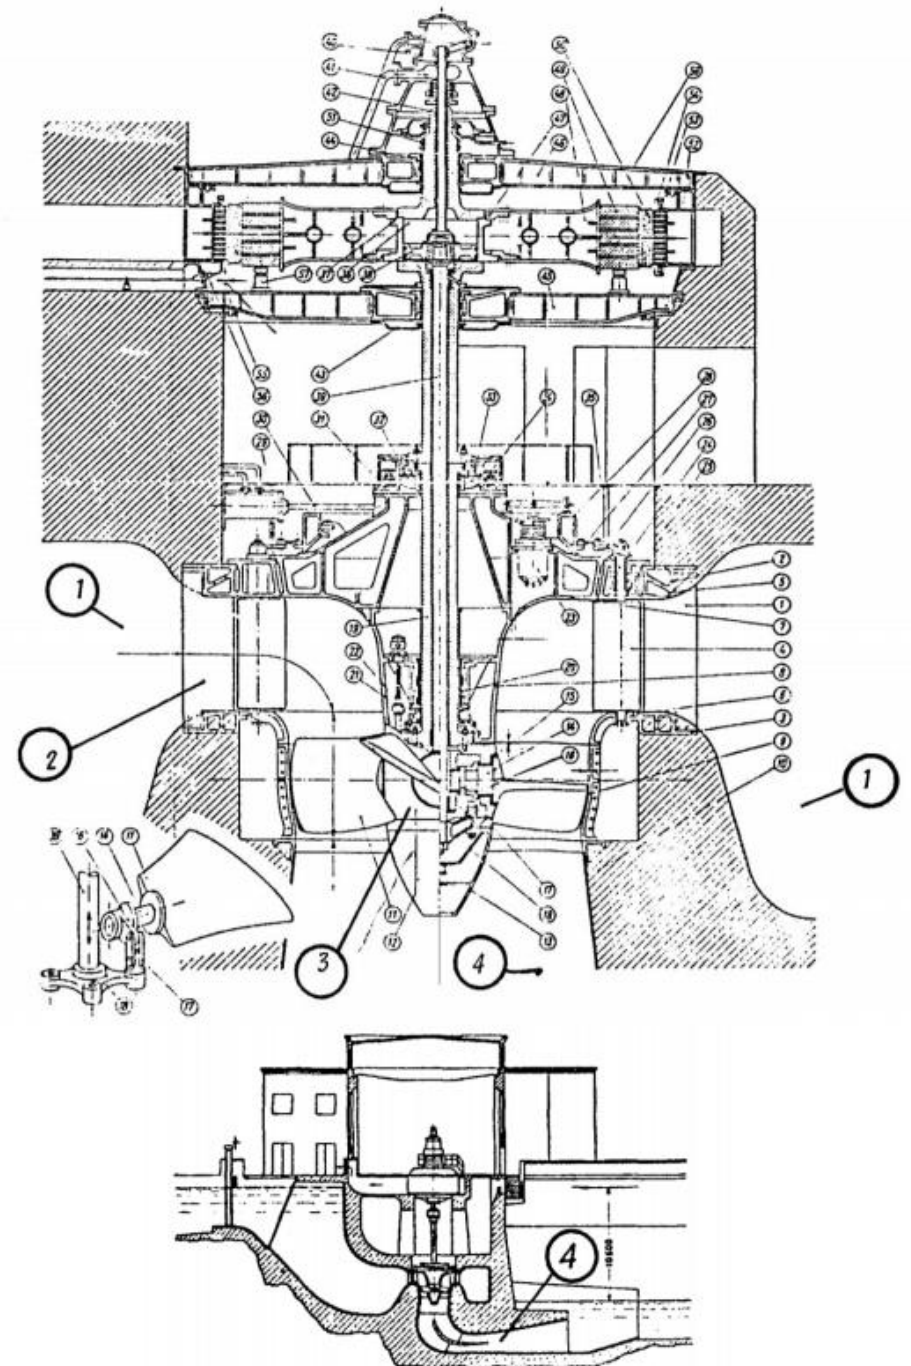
Planos de una turbina Kaplan. Fuente[24]
